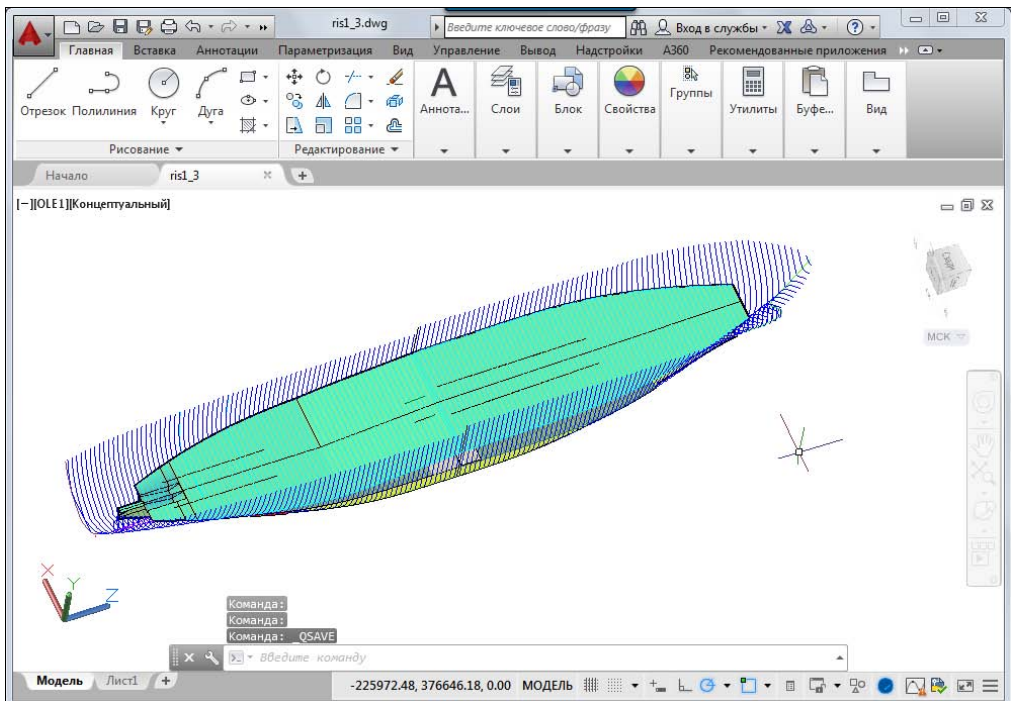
Трехмерная модель носовой и кормовой частей корпуса судна
